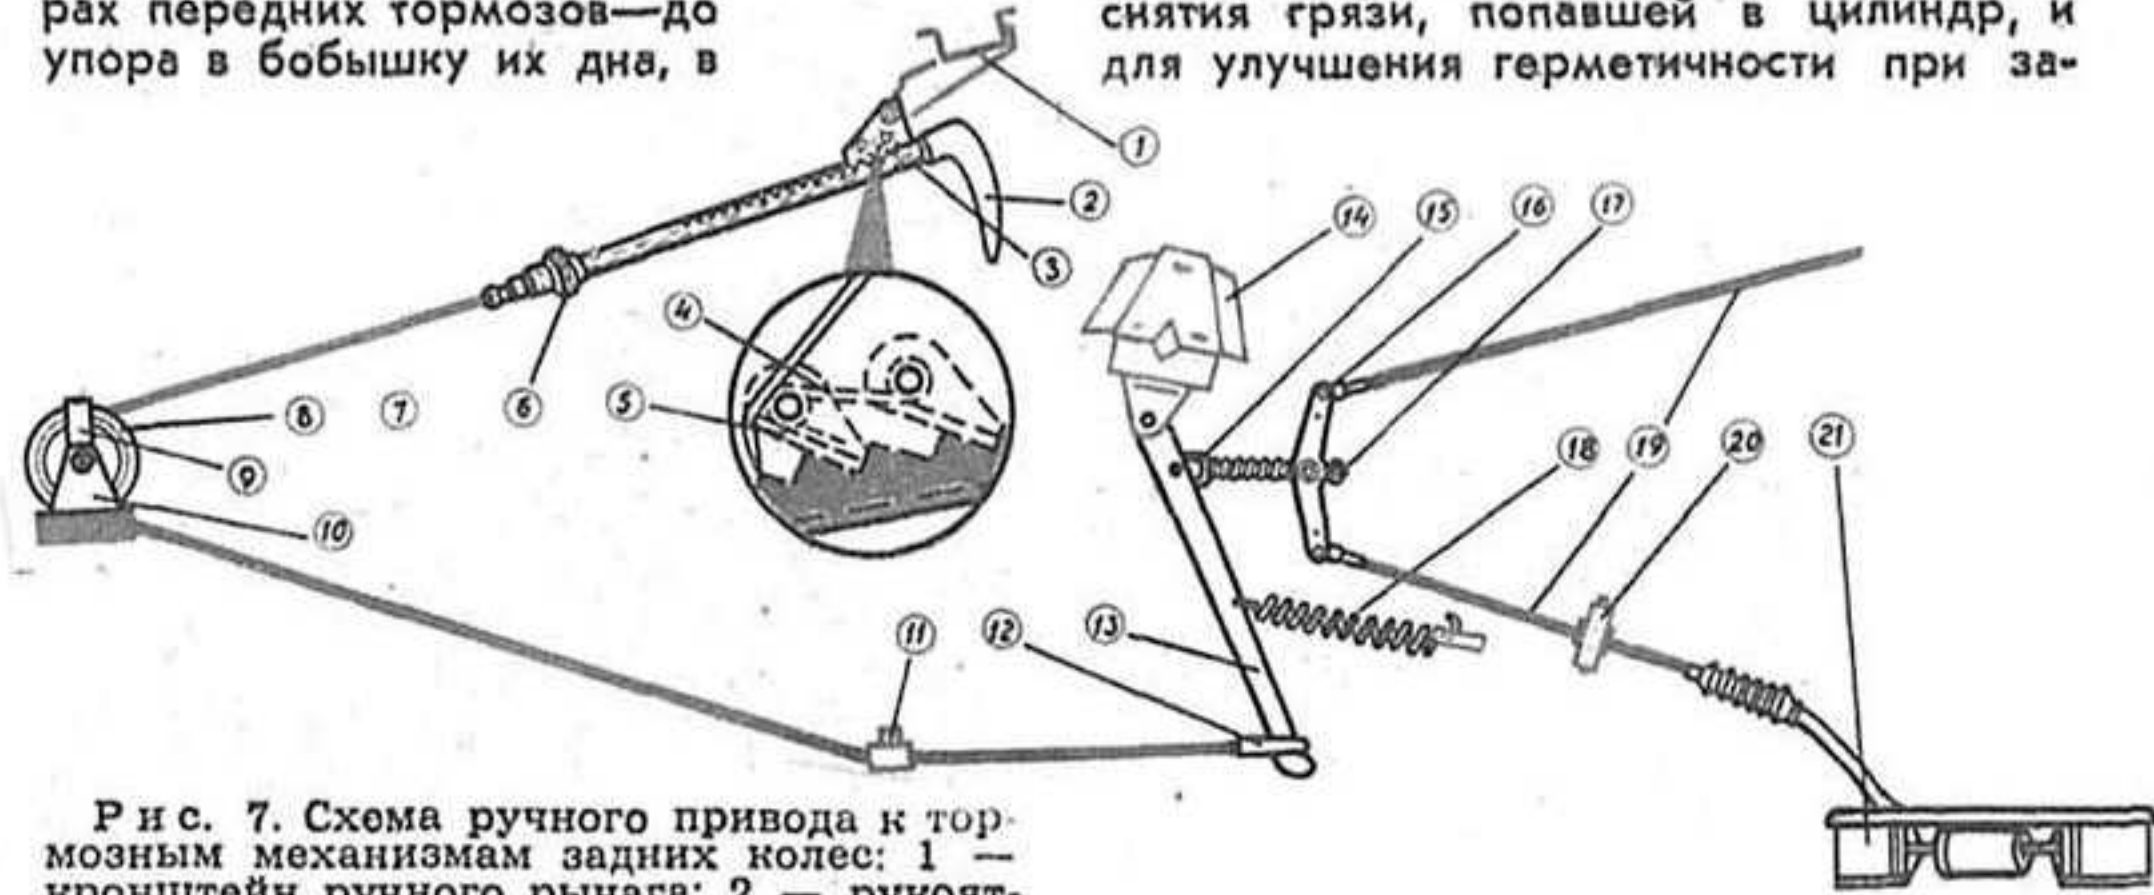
Схема ручного привода к тормозным механизмам задних колес: 1 — кронштейн ручного рычага; 2 — рукоятка со стержнем; 3 — корпус ручного рычага; 4 — пружина собачек; 5 — собачки; 6 — уплотнительная шайба; 7 — передний трос; 8 — ролик; 9 — ограничитель; 10 — кронштейн ролика; 11 — кронштейн переднего троса с пластмассовой втулкой; 12 — наконечник переднего троса; 13 — промежуточный рычаг; 14 — кронштейн промежуточного рычага; 15 — регулировочный наконечник; 16 — уравниватель; 17 — гайка регулировочного наконечника; 18 — оттяжная пружина; 19 — задние тросы; 20 — кронштейн задних тросов с резиновой втулкой; 21 — тормозной механизм заднего колеса.
